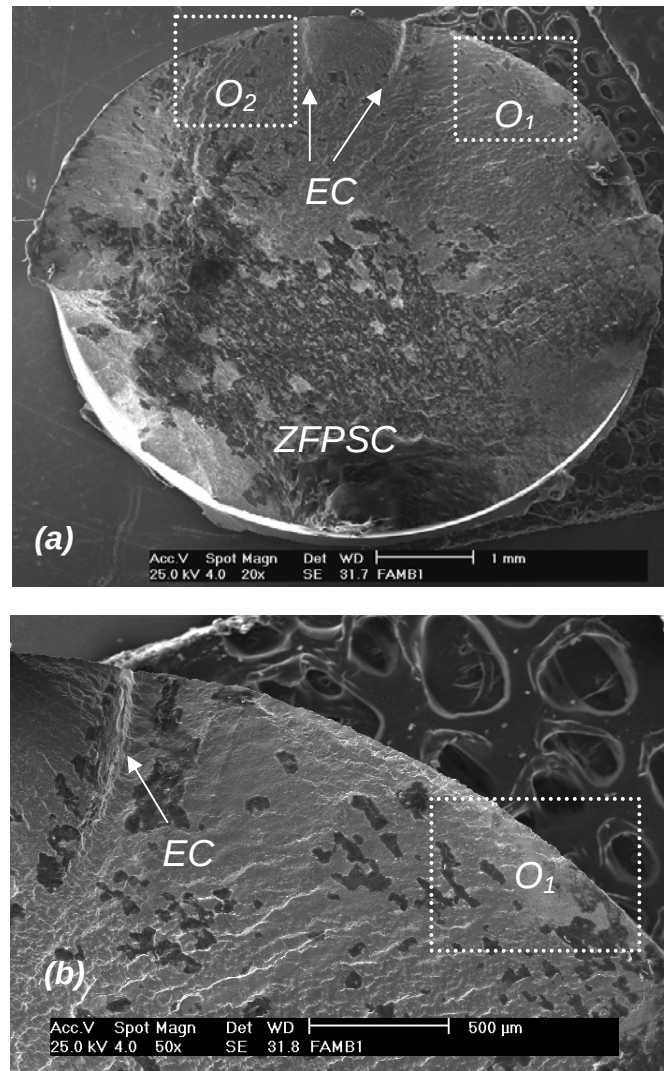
Superficie de fractura del material base a 754 MPa.
